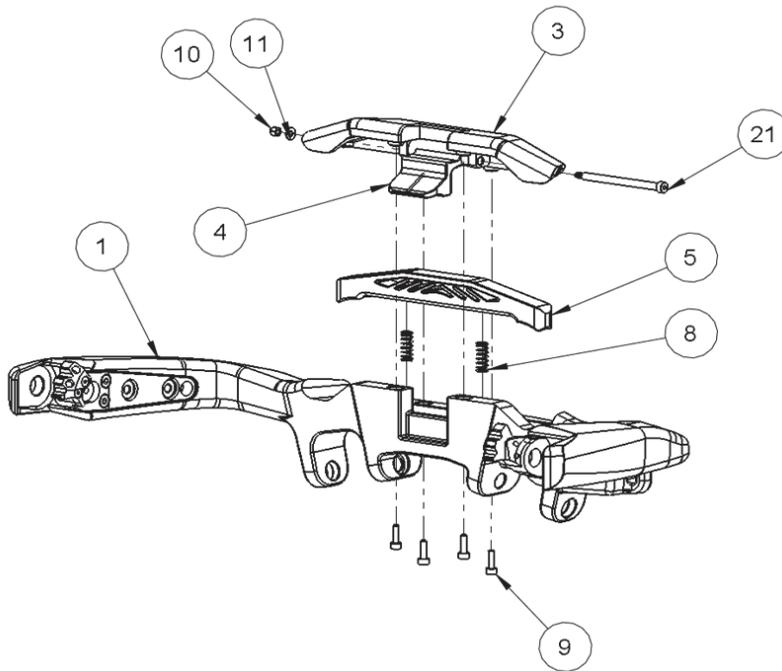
Vue éclatée — Assemblage arrière du scanner — Partie 1
